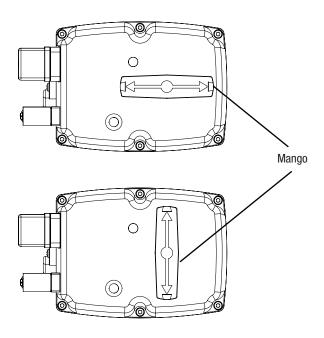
Vista en planta de accionamiento (izquierda: abierto; derecha: cerrado)
